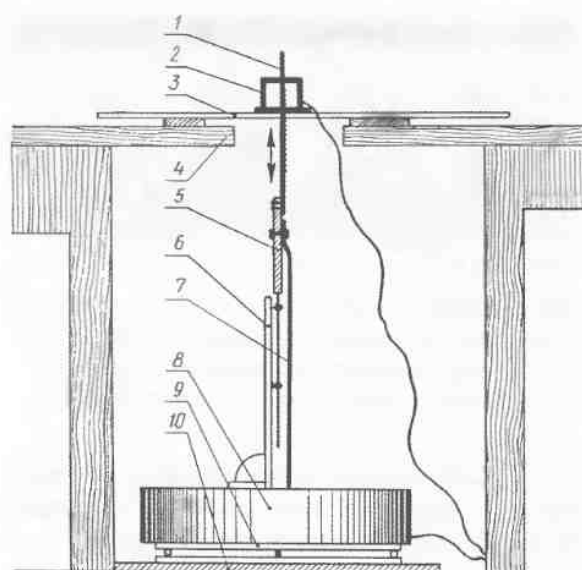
Принципиальная схема устройства механического лобзика: 1 — консольная пилка, движущаяся возвратно-поступательно в кондукторе; 2 — кондуктор; 3 — выпиливаемая доска; 4 — опора доски; 5 — ползун, соединенный с пилкой; 6 — стойка с направляющими кольцами для ползуна; 7 — шатун, соединяющий ползун с вращающимся колесом внутри кожуха; 8 — кожух; 9 — поворотный диск; 10 — войлочная подкладка
